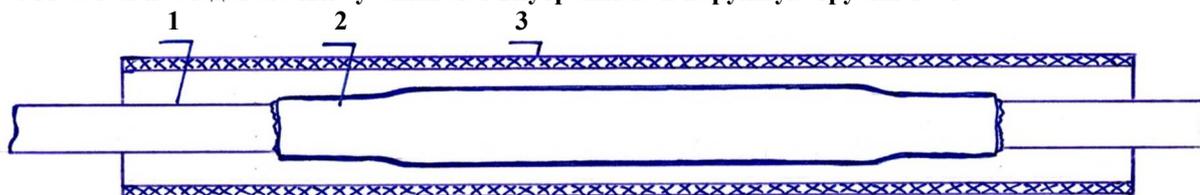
Усадка внутренней ТУТ и подготовка к усадке наружной ТУТ:
